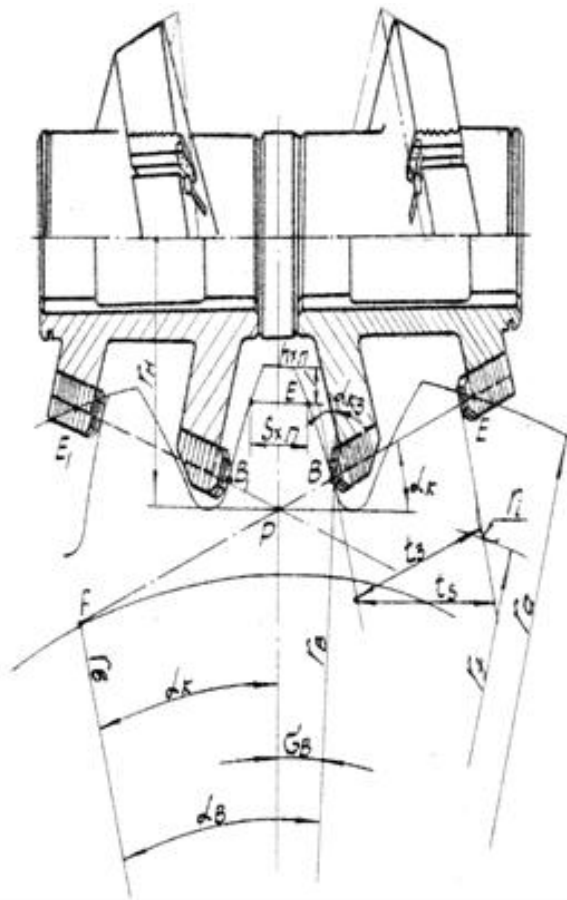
Схема станочного зацепления специальной твердосплавной фрезы с обрабатываемым колесом
